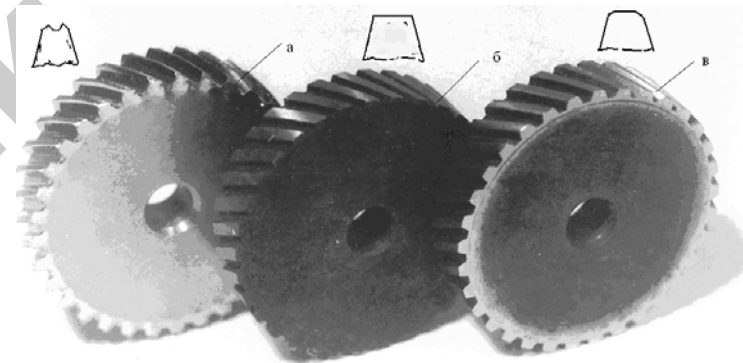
Фотографии заготовок зубчатого колеса:
